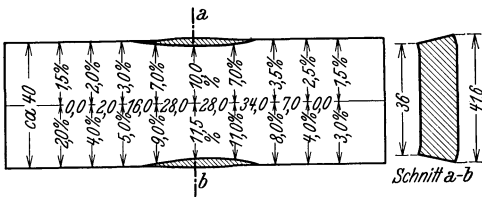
Ausmessung der Dehnung einer Schweißbiegeprobe bei einer quadratischen oder rechteckigen Einteilung der Schweißzone.
